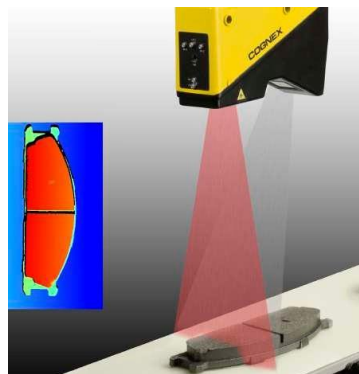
Sistema de visión 3D con cámaras múltiples (Introducción a la visión artificial, 2021)
